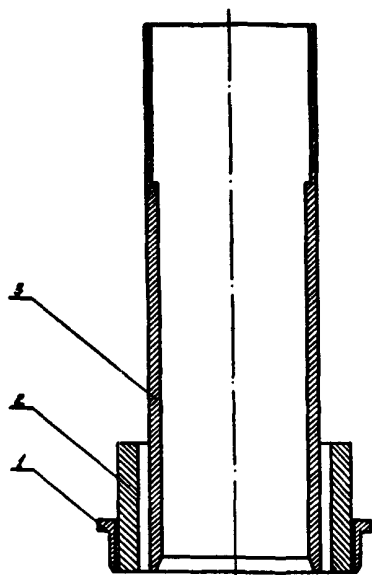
Приспособление для оборки скользящих контактов отделителя:
